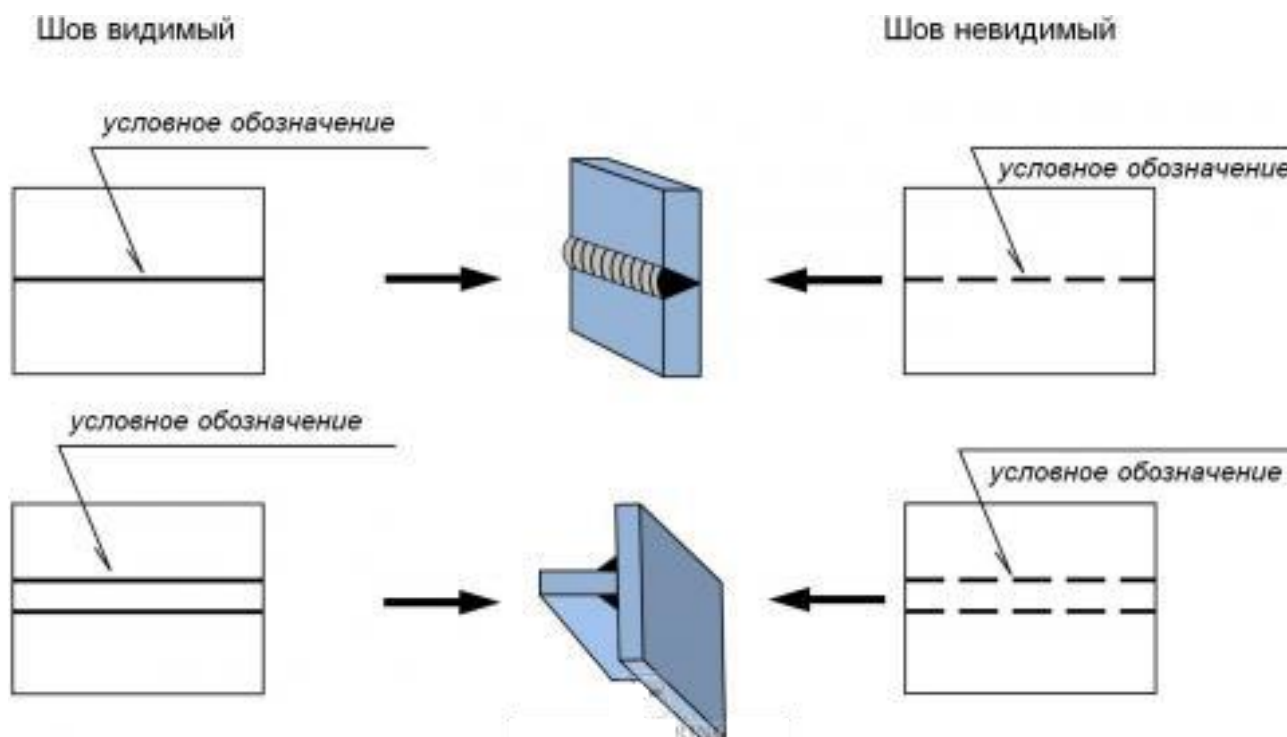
Расположение условного обозначения сварных швов
